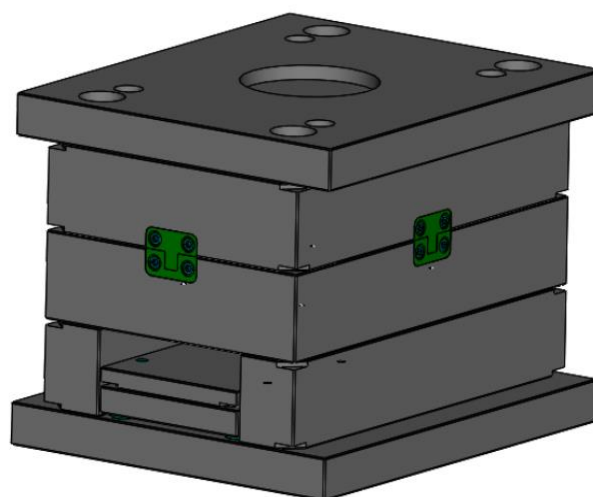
Representação dos rasgos de desmontagem das chapas no molde.
